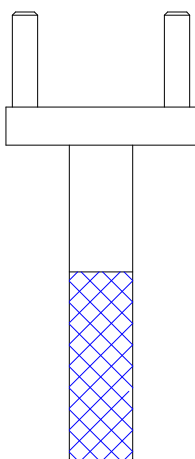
Desenho da ferramenta para fixação e remoção das partes do radiômetro
